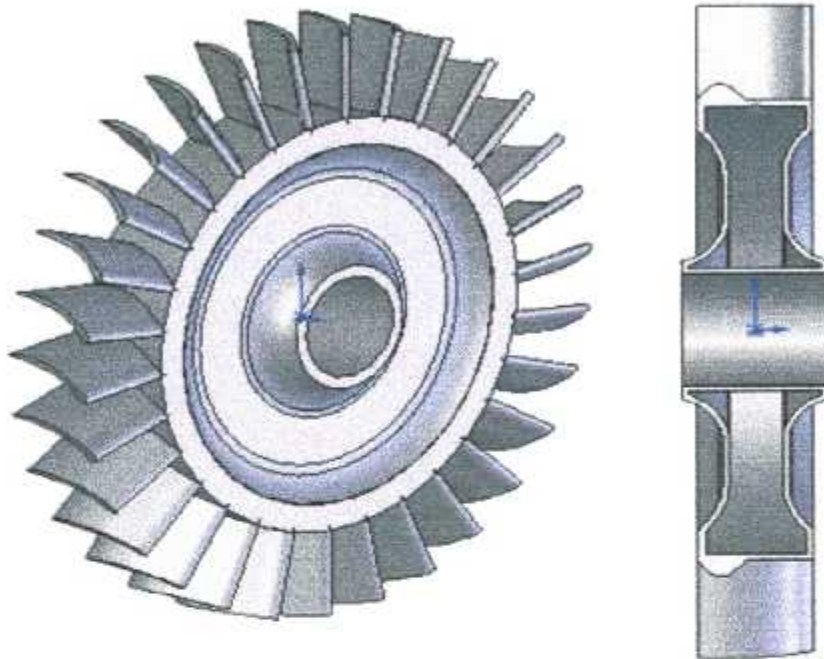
vue en coupe et en perspective de la roue de la turbine.
